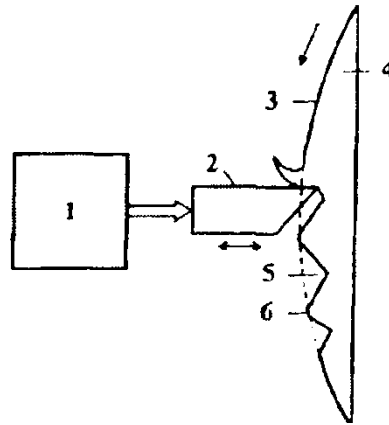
Схема виготовлення форм глибокого друку гравіюванням 1. система електронного керування рухом різця, 2. різець, 3. поверхня формного циліндра; 4. формний циліндр; 5. друкуючий елемент; 6. пробільний елемент
